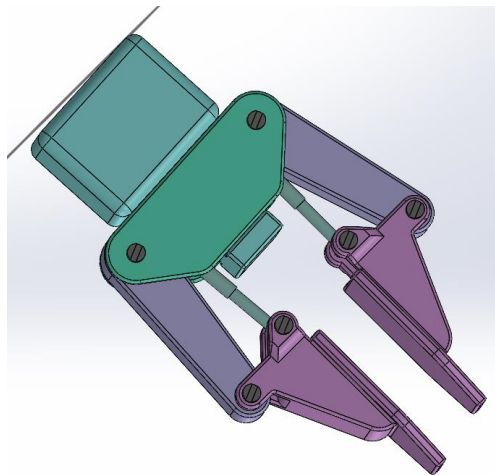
3D модель механічного захоплюючого пристрою для деталей типу «Корпус»
